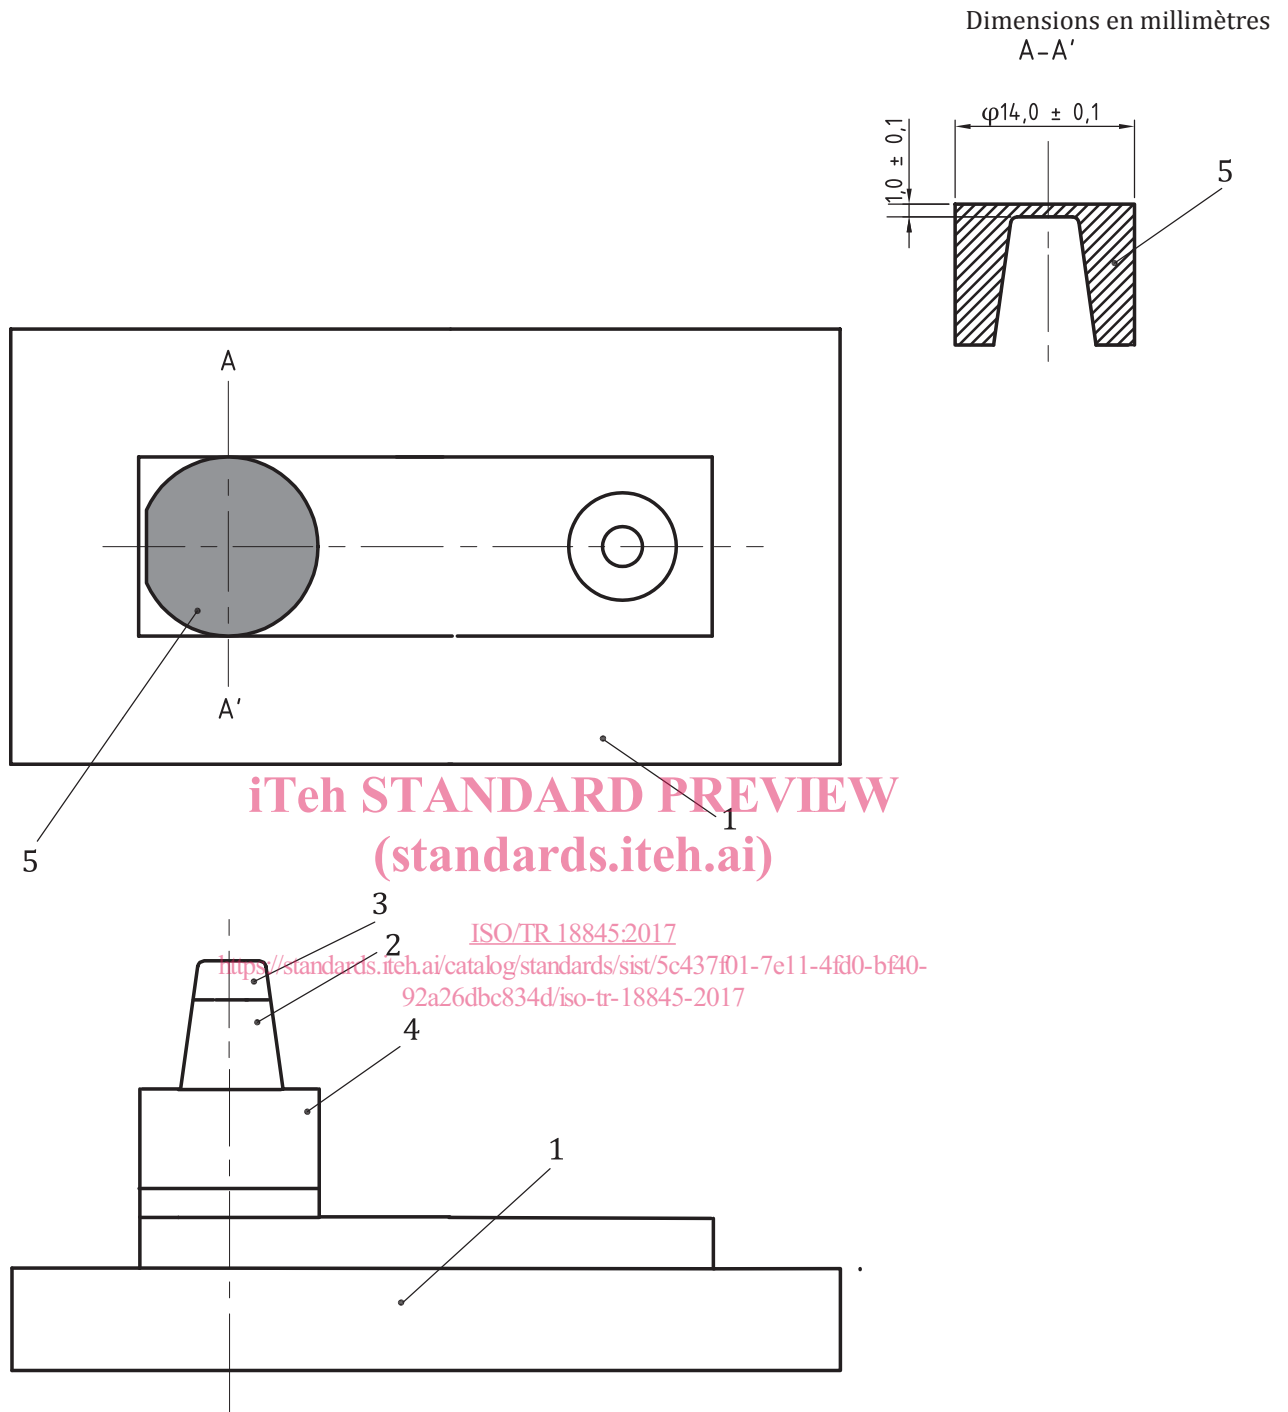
Modèle pour éprouvette d'inlay de classe II
